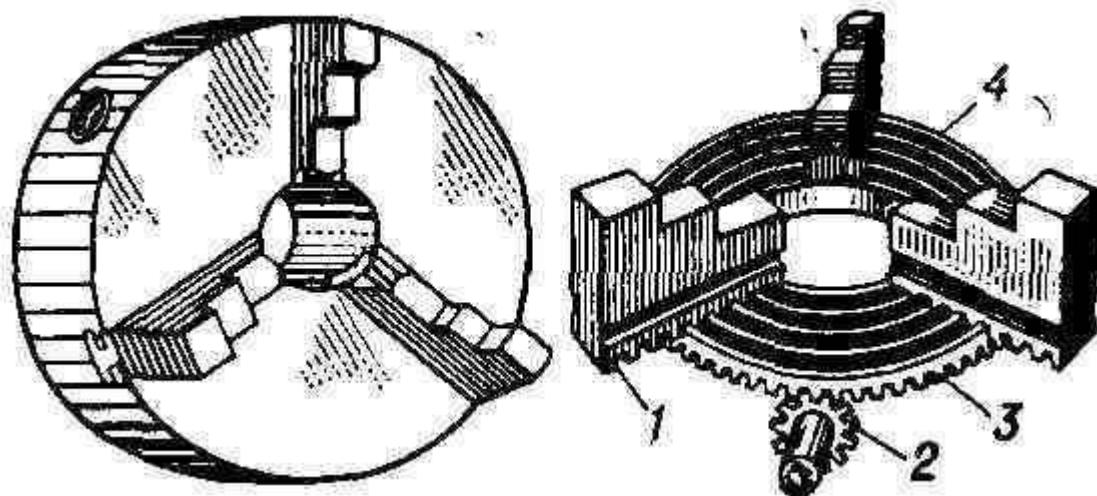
Трехкулачковый патрон: 1 – кулачок; 2 – коническая шестерня; 3 – зубчатое колесо; 4 – спиральная канавка.
